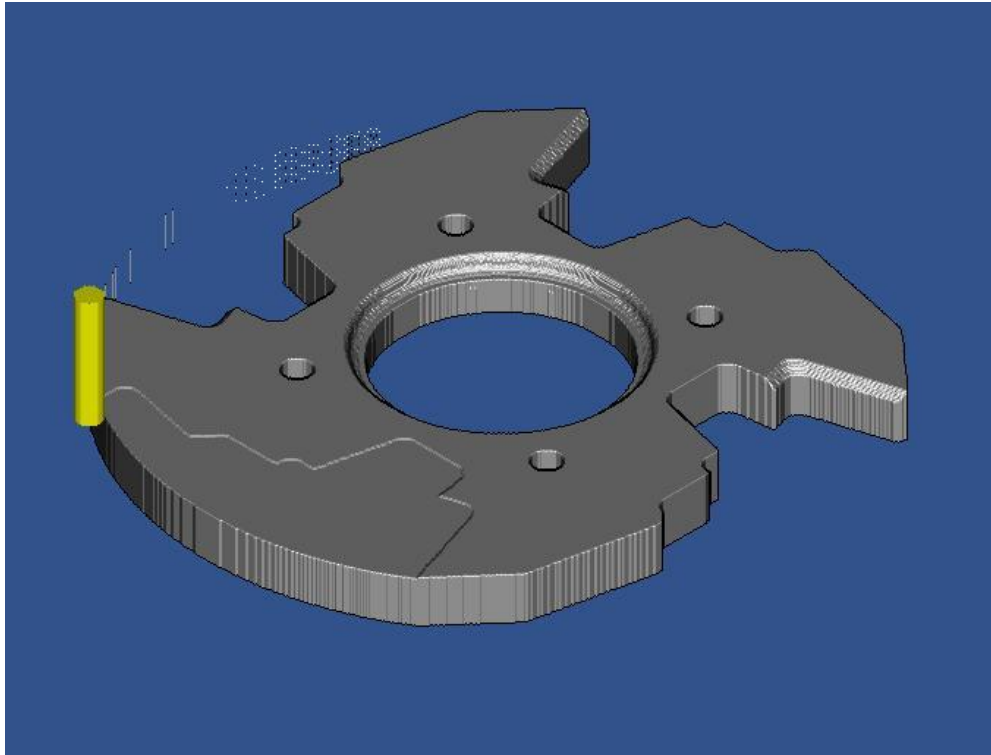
Траєкторію руху різця під час чорнової обробки
